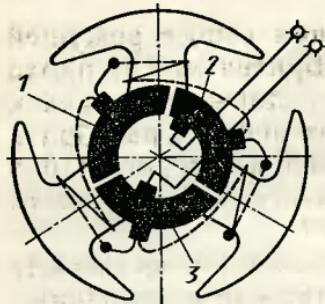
Схема намотки якоря (вид со стороны коллектора):
